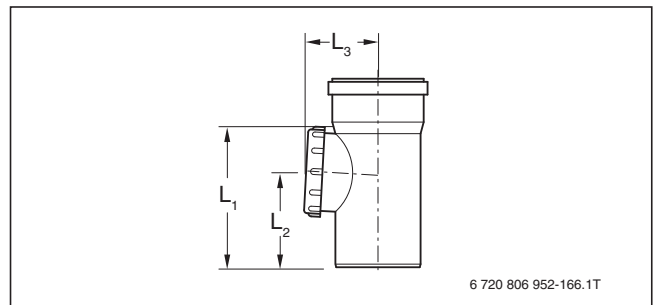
Rohr mit Prüföffnung GB225 (Maße in mm)
